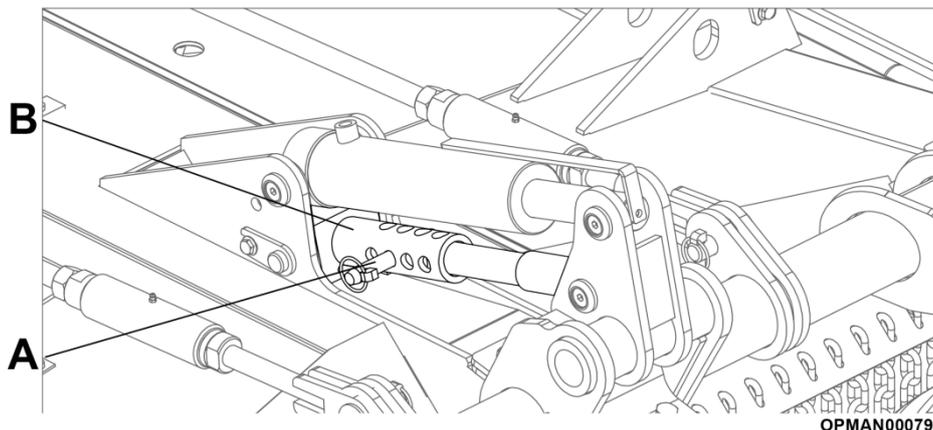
Multicut 460/620 Minimaler Höhenanschlag
